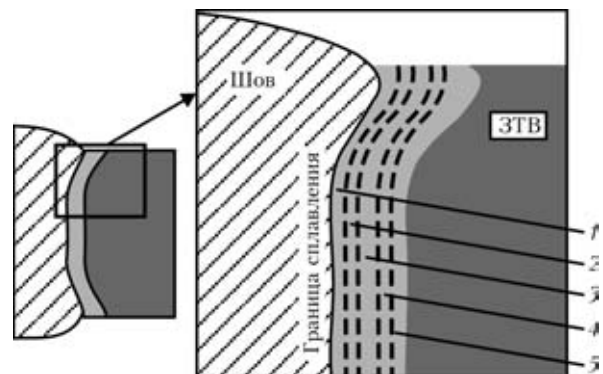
Схема сварного соединения с различными структурными зонами, образующимися при сварке плавлением алюминий-литиевого сплава: 1 – перегрев; 2 – закалка; 3 – отжиг; 4 – отпуск; 5 – старение
